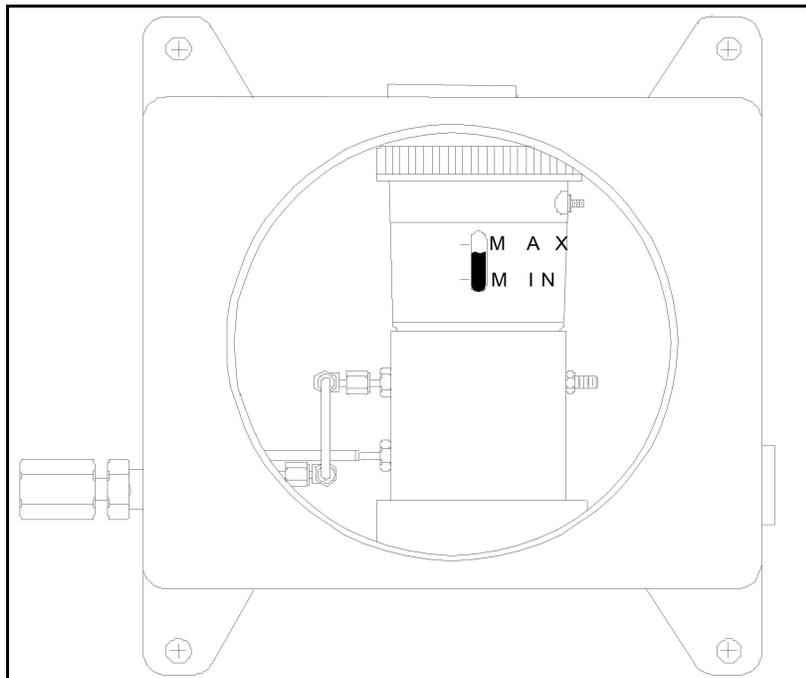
Explosionsgeschützte Delta F-Sauerstoffzelle
